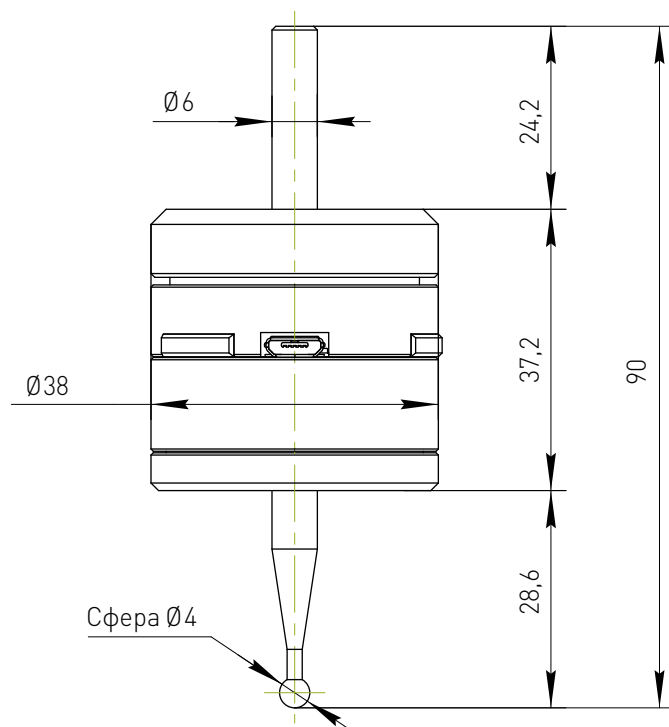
Габаритные размеры модуля датчика PLL006.
